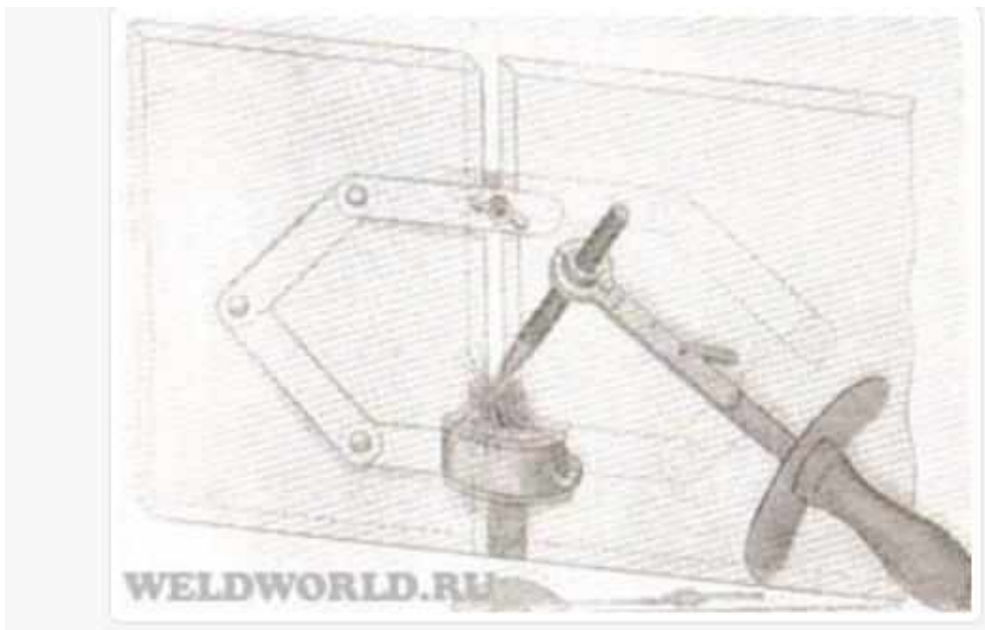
Aparelho de soldagem vertical ascendente – Weldworld.ru
